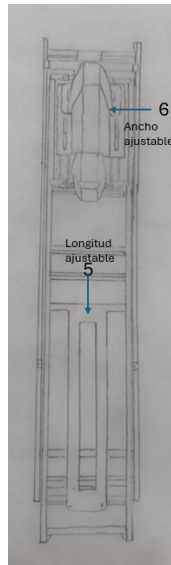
, Boceto de alternativa N°1 elevador tipo rampa
